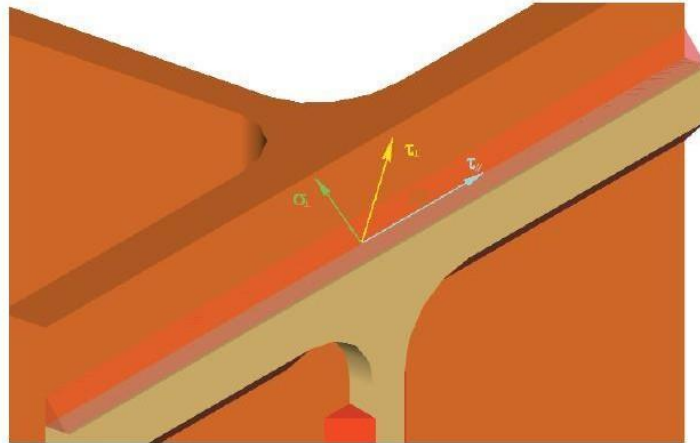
Descomposición de los esfuerzos transmitidos al cordón de soldadura.
